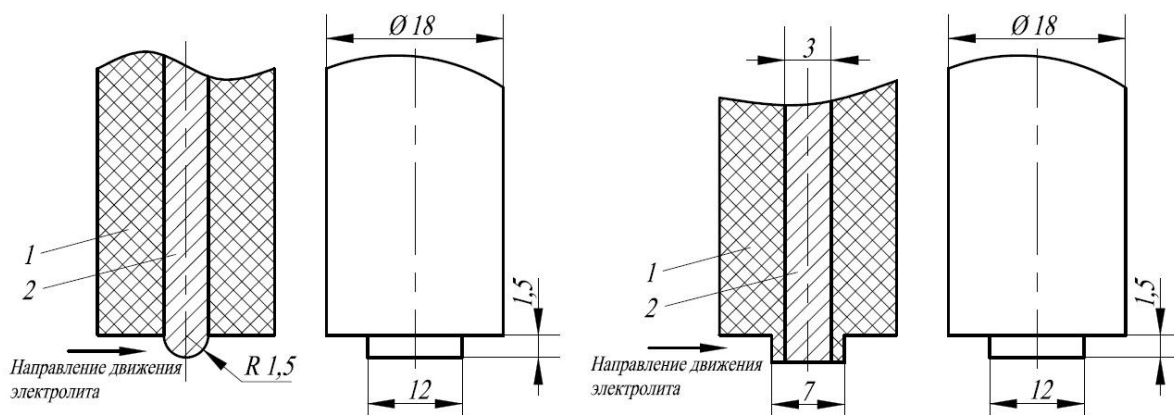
Форма катода-инструмента: а – выпуклая рабочая поверхность; б – плоская рабочая поверхность
